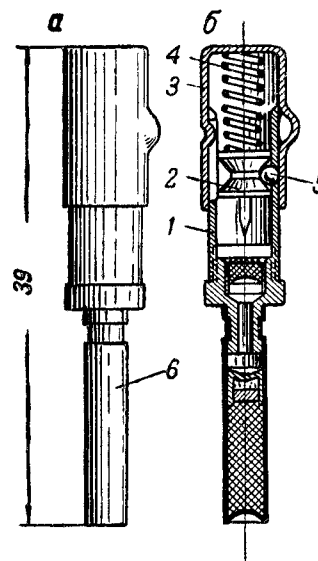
Минный взрыватель пятого образца (МВ-5):
